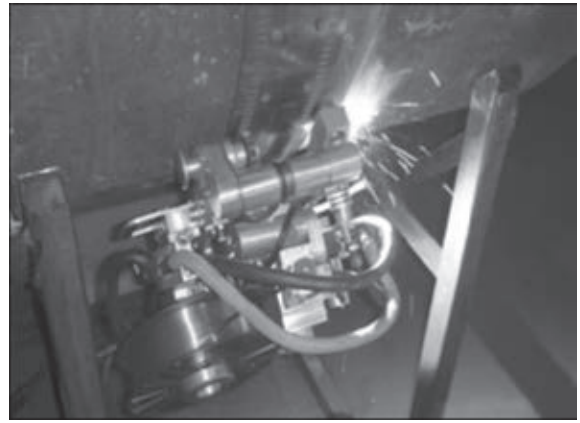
Система сварки неповоротных швов фирмы «ИТС» (Россия)
